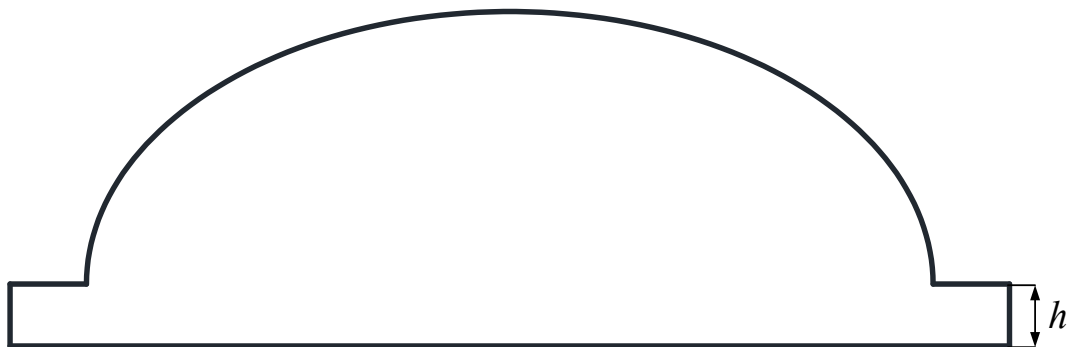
Форма заготовки из листа диэлектрика
